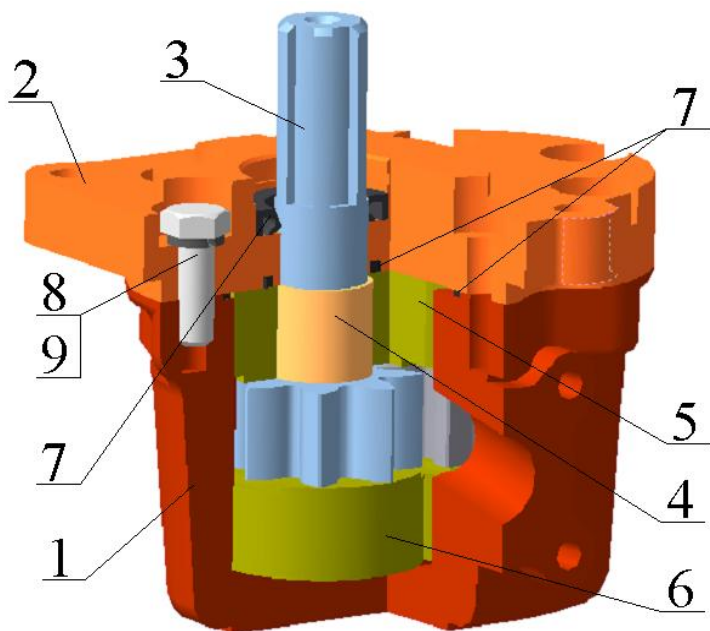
Шестеренный насос конструктивного исполнения «УК»: 1 – корпус; 2 – крышка; 3 – шестерня ведущая; 4 – подшипники; 5 – компенсаторы; 6 – манжета резиновая; 7 – резиновое уплотнение; 8 – болт; 9 – шайба пружинная
